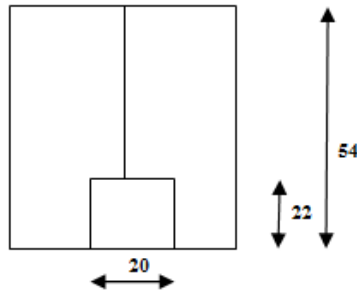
Esquema de longitud de la soldadura
